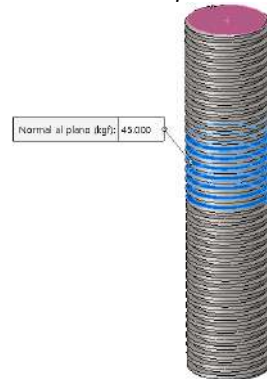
Carga aplicada en el sector de la rosca hembra (60mm, 7,09 hilos).
